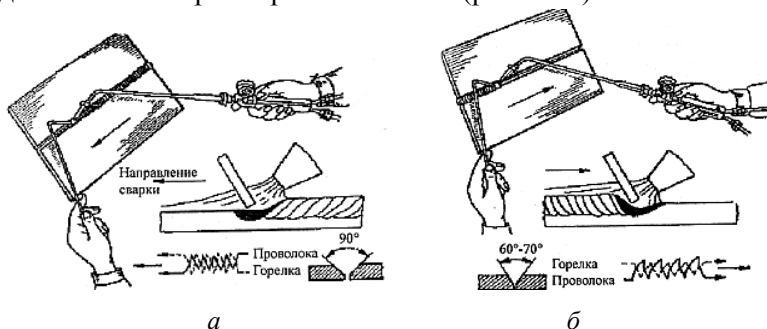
Левый (а) и правый (б) способ сварки:
